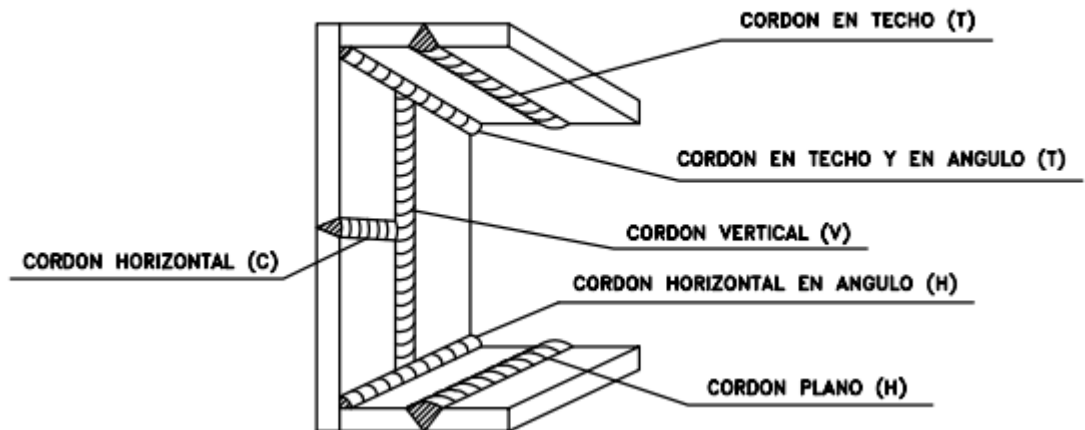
Soldadures segons la posició del cordó durant la operació (Font: Universidad de Castilla la Mancha)
